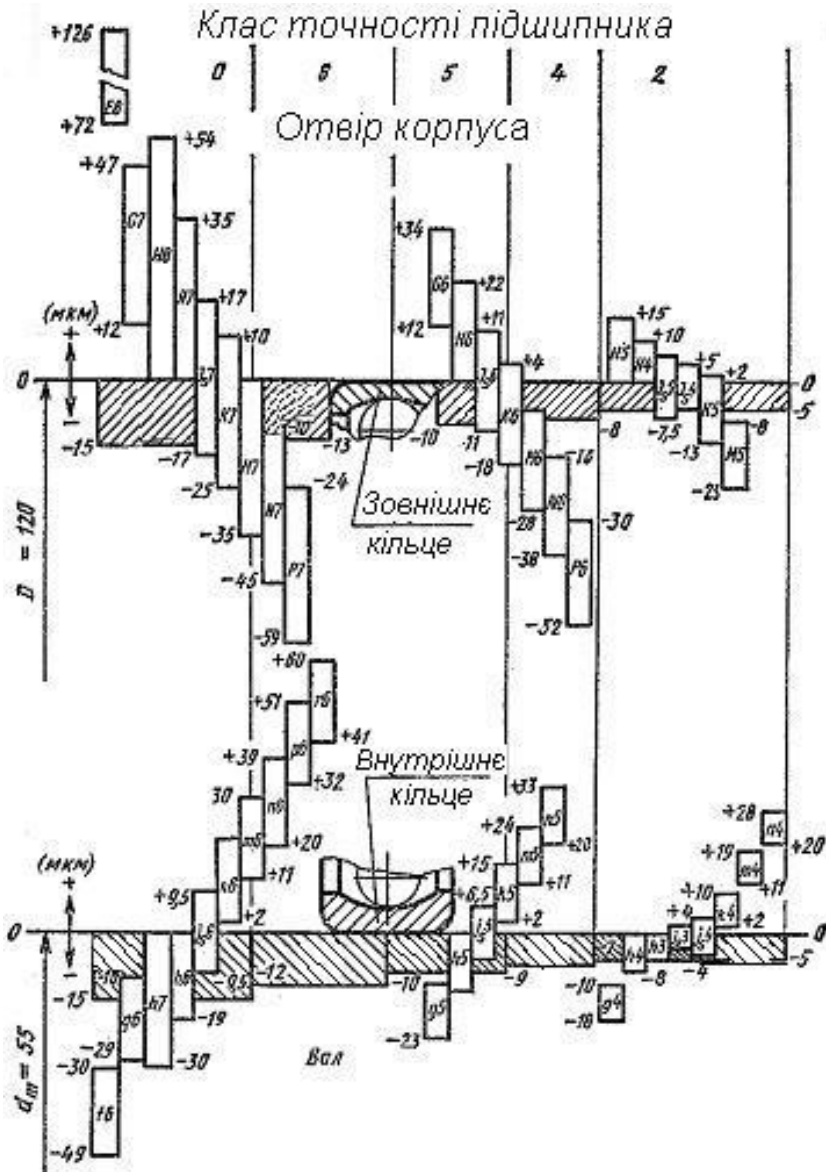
Схема розташування рекомендованих полів допусків підшипників і з'єднаних з підшипниками поверхонь
